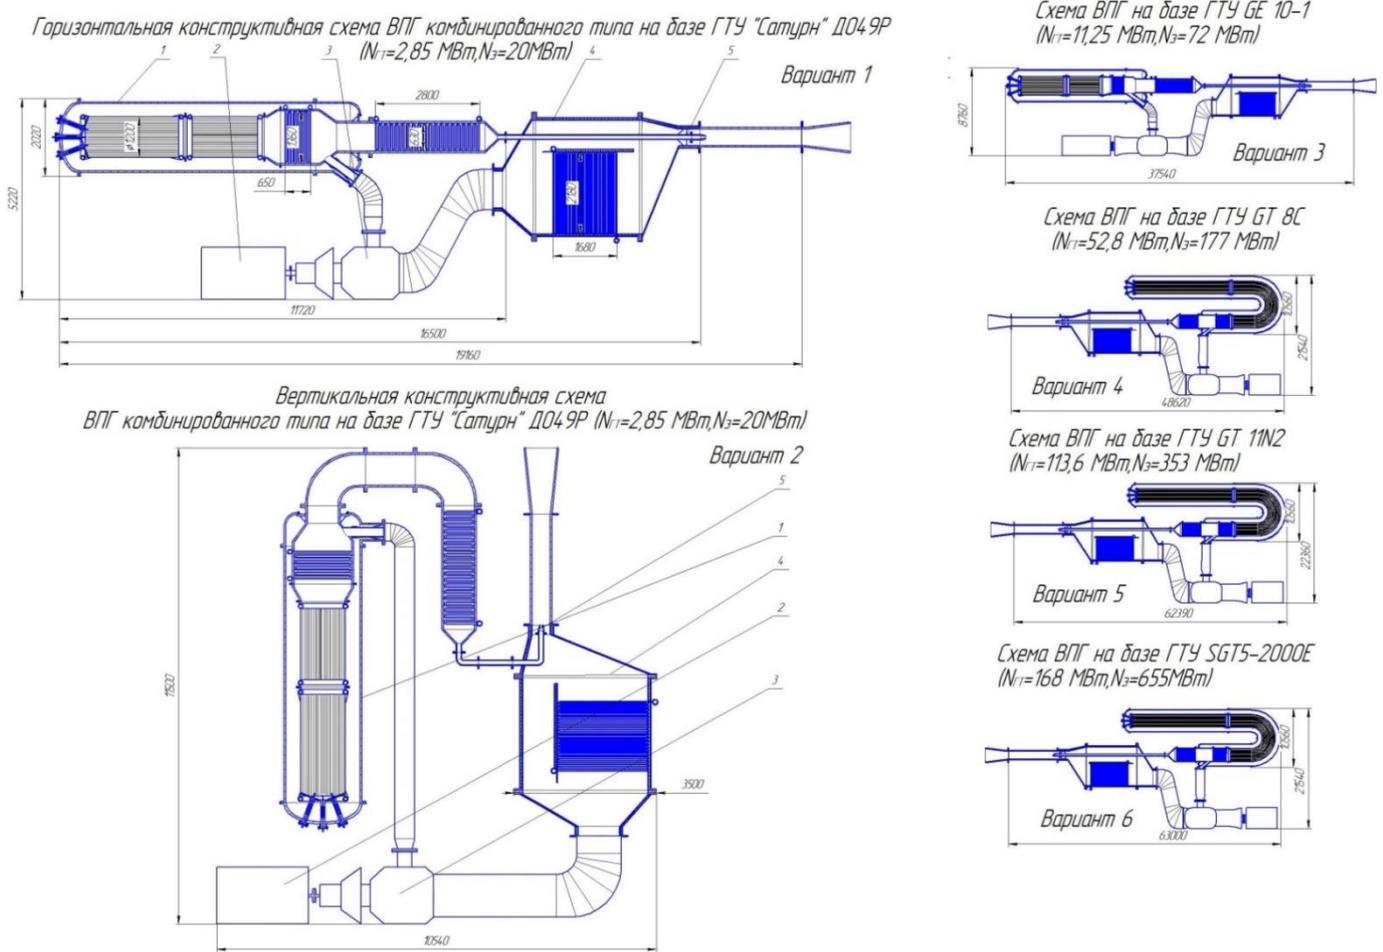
Предлагаемые компоновочной схемы и типоразмеры ПГУ с ВПГ
